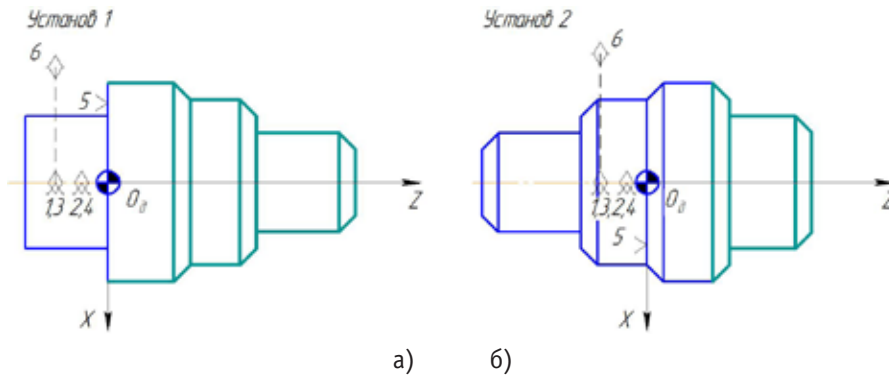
Эскиз обработки вала: Установ 1 (а) и Установ 2 (б)
